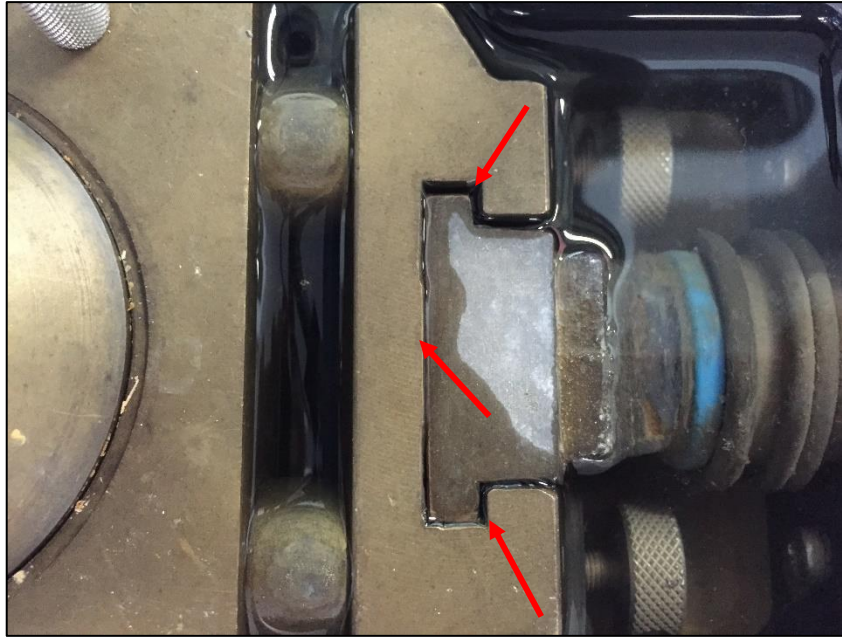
Ensamble caja-brazo de máquina Shearmatic
